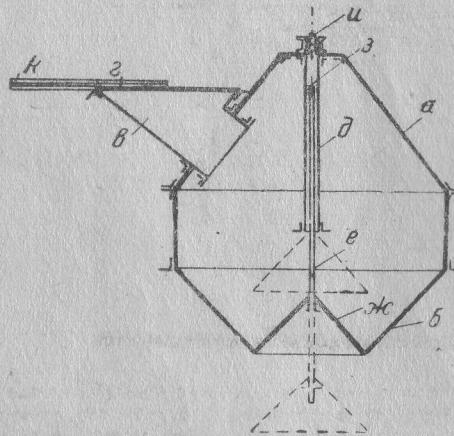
а—железный кожух; б—воронка; в—приемная воронка; г—крышка приемной воронки; д—направляющая подвижной штанги; е—подвижная штанга; ж—полый конус; з—трос; и—блок; к—угловое железо (для подъема крышки рамой ковша ската).
